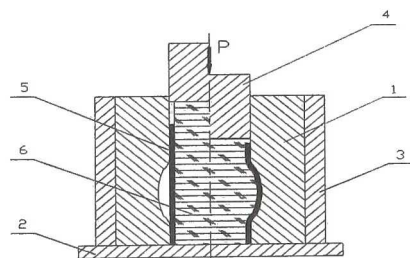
Штамп для раздачи трубчатой заготовки с использованием стержня из льда или снега
